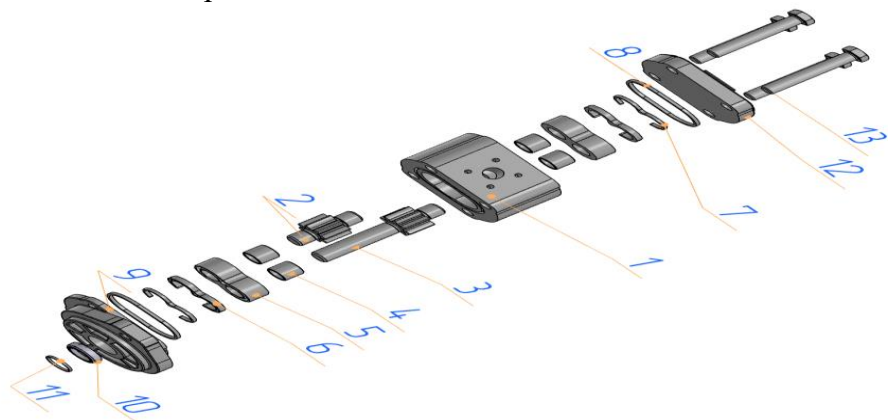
Шестеренный насос GP2K10: 1- корпус; 2 - шестерня с валом ведомая; 3 - шестерня с валом ведущая; 4 - антифрикционная втулка; 5 - корпус подшипника; 6 - манжета торцевого уплотнения; 7 - пластина защитная; 8 - кольцо уплотнительное; 9 - монтажный фланец; 10 - манжета уплотнения вала; 11 - кольцо стопорное; 12 - крышка; 13 - болт
